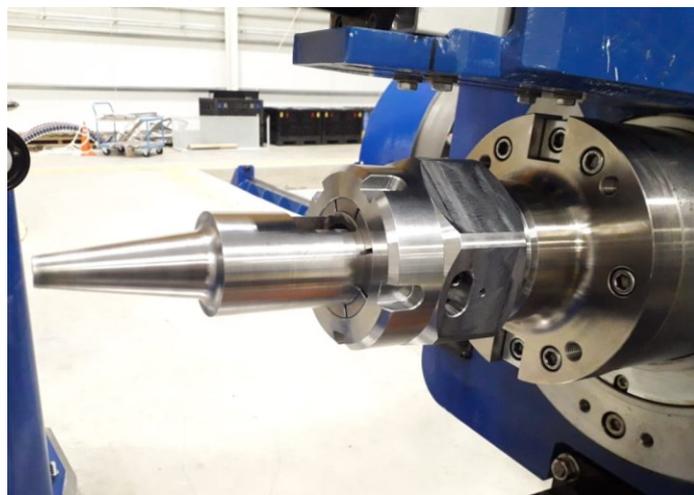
Cabezal de soldadura centro de FSW.
